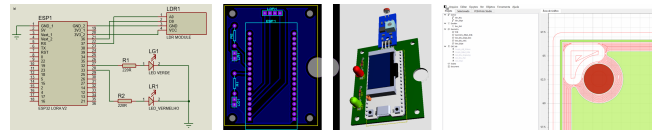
Processo didático de desenvolvimento de PCB: (a) esquemático eletrônico do circuito; (b) layout da placa; (c) visualização 3D dos componentes montados na PCB; (d) geração do código para confecção de placa PCB na CNC.
